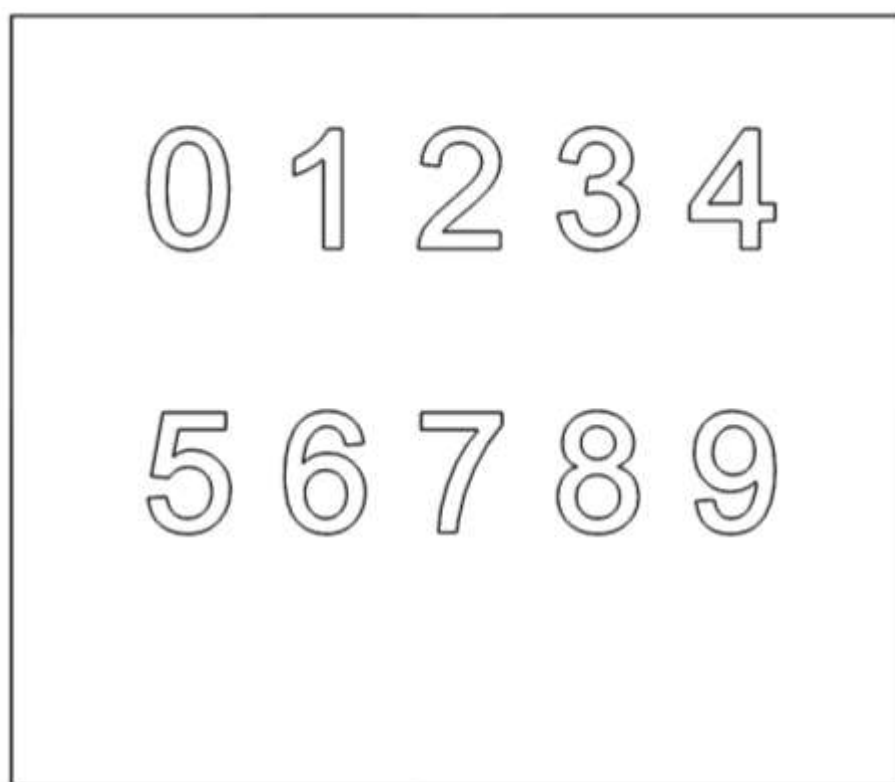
Контур цифр для лазерного обрбления.
